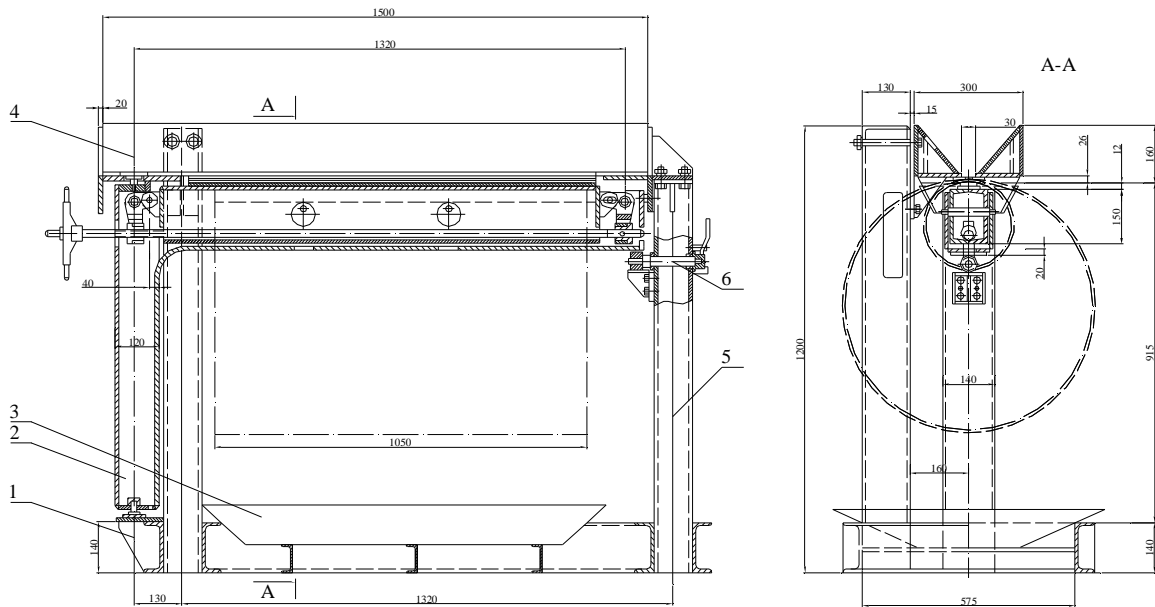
Установка для сварки продольного шва обечайки.
